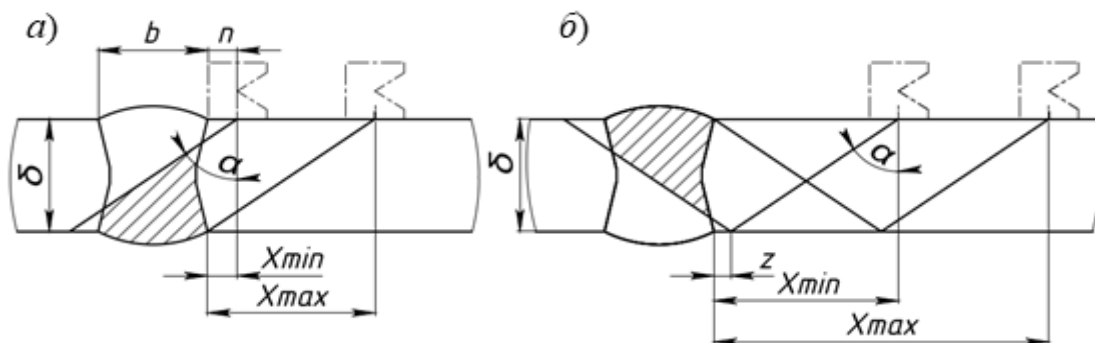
Схемы контроля стыковых сварных соединений прямым (а) и однократно отражённым (б) лучом
